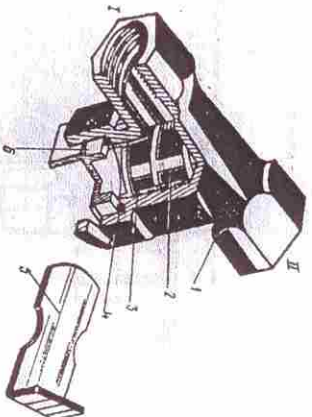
Фильтр магистральный: 1 — корпус; 2 — элемент фильтрующий; 3 — лунка; 4 — кольцо уплотнительное; 5 — пластина; 6 — крышка
